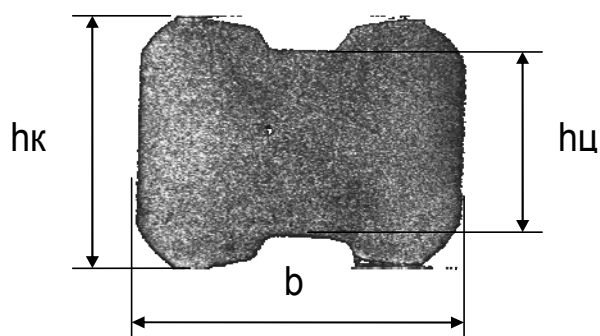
Вид профиля поперечного сечения металла после протяжки в калибре
